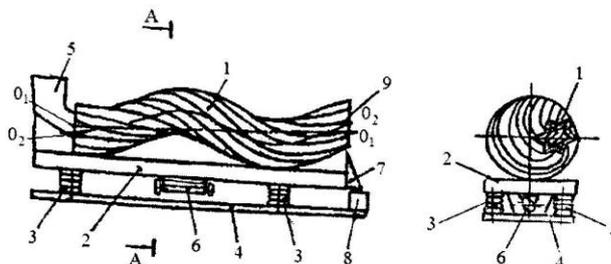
Станок для отделочно-зачистной и упрочняющей обработки деталей машин с спиральным, прамоточным рабочим органом снабженным карманами треугольной формы (1 - рабочий орган станка; 2 - платформа; 3 - четыре резинокордных баллона; 4 - основание; 5 - загрузочное устройство; 6- вибратор; 7 - склиз, 8 -разгрузочное устройство, 9 - разгрузочное окно)
